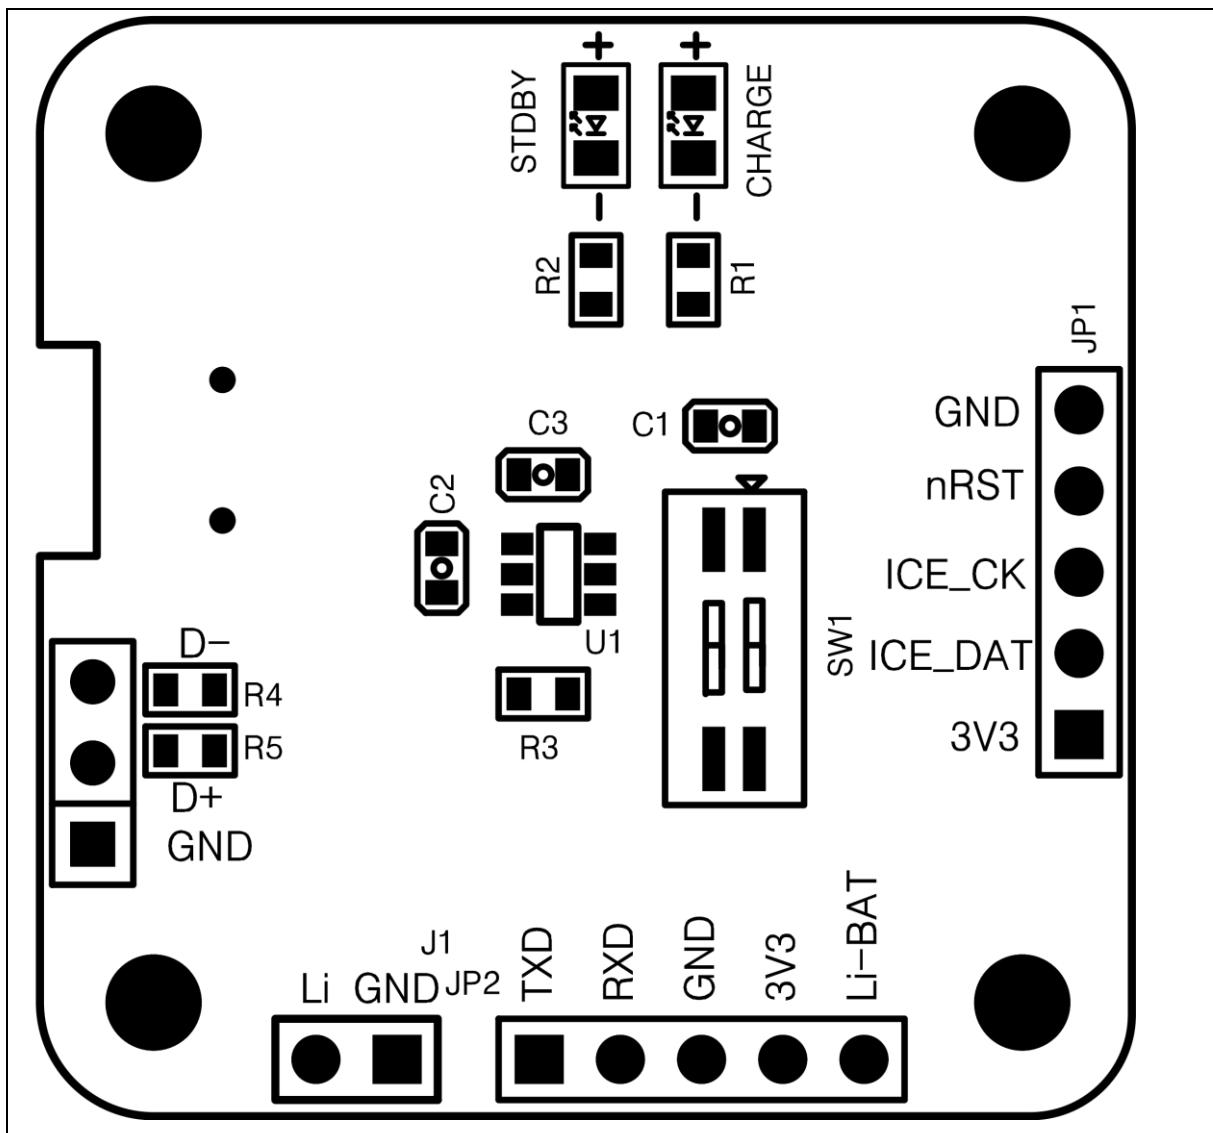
AHRS 模組通信端正面 PCB 佈局
